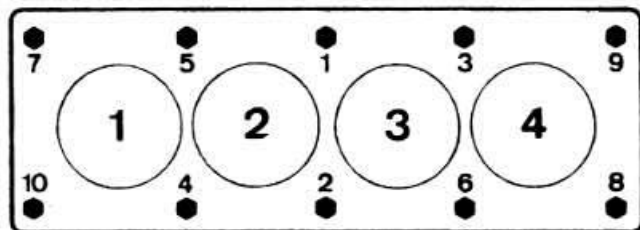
Порядок затяжки болтов головки цилиндров двигателя М40
